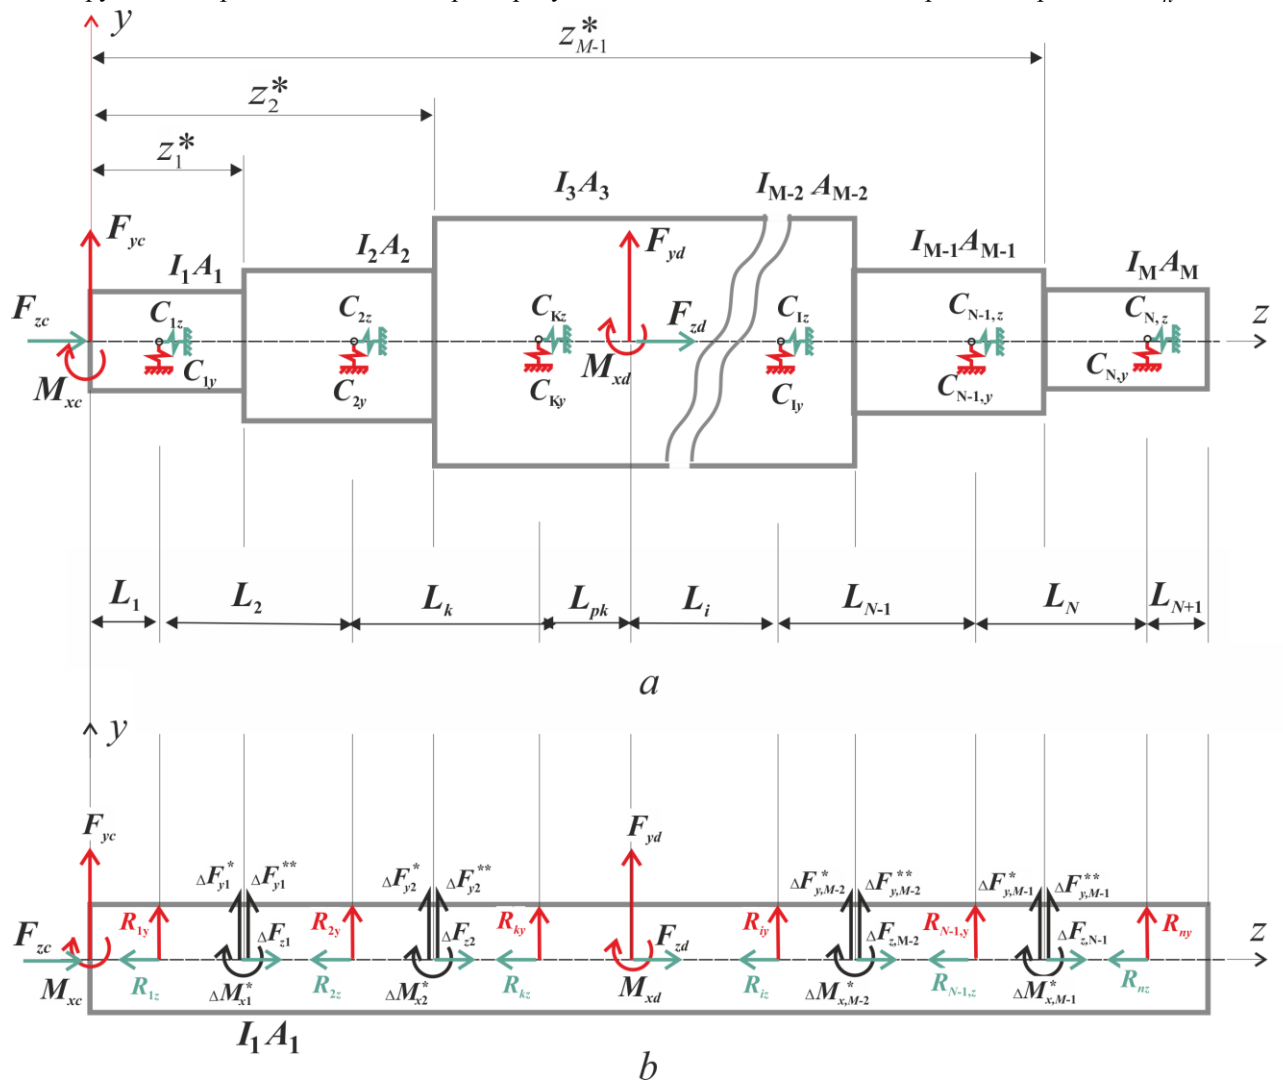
Розрахункова схема багато опорного ступінчатого шпиндельного валу
